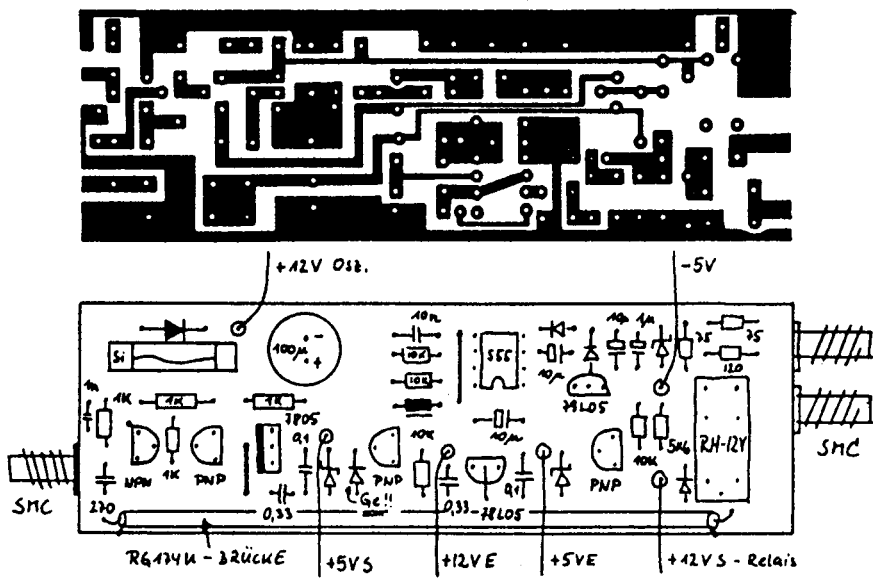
Platine, pcb. (Weißblechgehäuse, box 111x37x30mm Typ 3)
